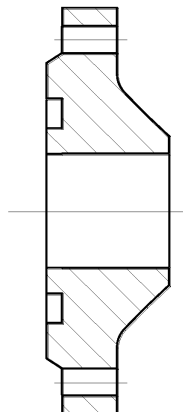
а – Конструкции фланцев стальных приварных встык
